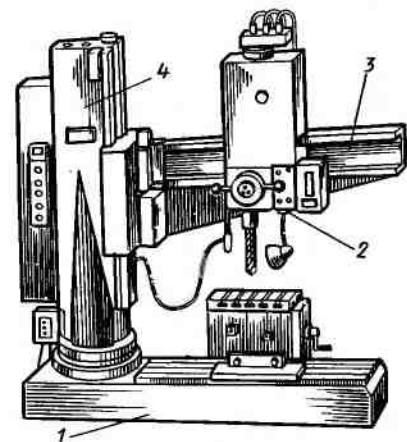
Общий вид радиально-сверлильного станка мод. 2554
